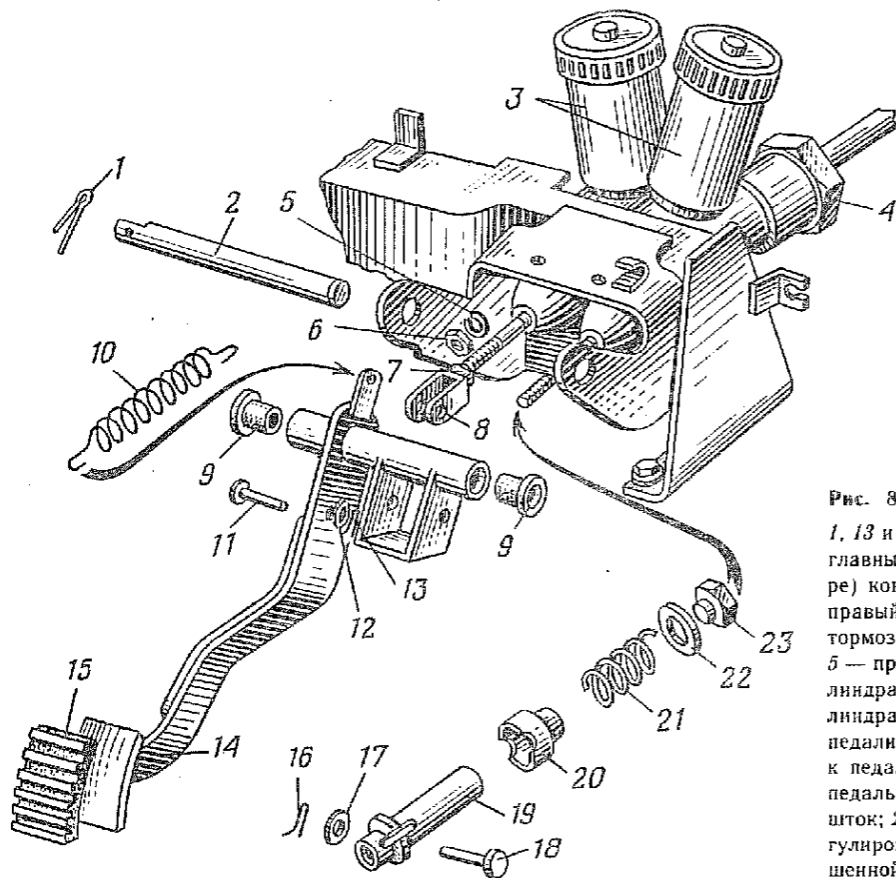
Привод главных тормозных цилиндров: 1, 13 и 16 — шплинты; 2 — ось педали тормоза; 3 — главные цилиндры тормоза: левый (с дет. 7 и 8 в сборе) контура гидропривода тормозов передних колес; правый (с дет. 19—23 в сборе) контура гидропривода тормозов задних колес; 4 — соединительная гайка; 5 — пружинная шайба; 6 — гайка крепления цилиндра; 7 — контргайка; 8 — вилка толкателя цилиндра; 9 — втулка педали; 10 — оттяжная пружина педали; 11 — палец крепления оттяжной пружины к педали левого цилиндра; 12 и 17 — шайбы; 14 — педаль тормоза; 15 — накладка; 18 — палец; 19 — шток; 20 — упорная шайба; 21 — пружина; 22 — регулировочная шайба (только для автомобилей повышенной грузоподъемности); 23 — специальная гайка
